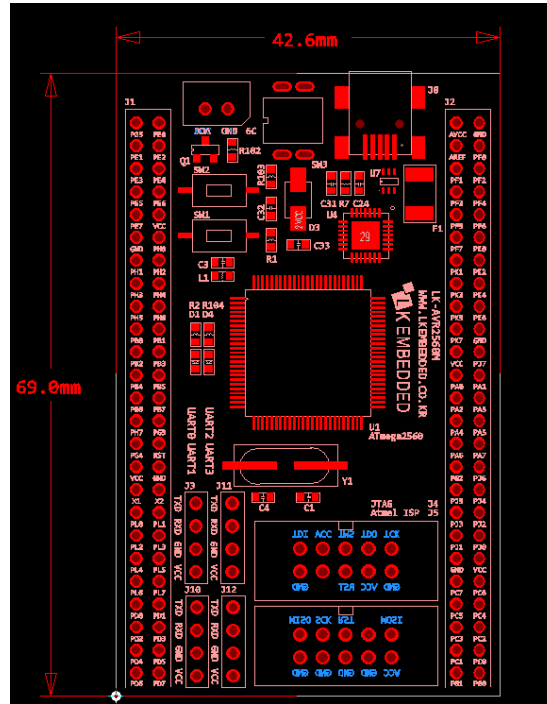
ATmega2560 개발모듈 PCB 설계도면 그래픽 사진
